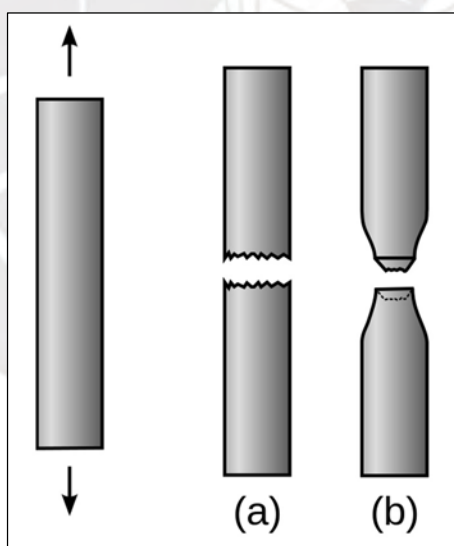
Tipos de fractura: (a) fractura frágil y (b) fractura dúctil.
